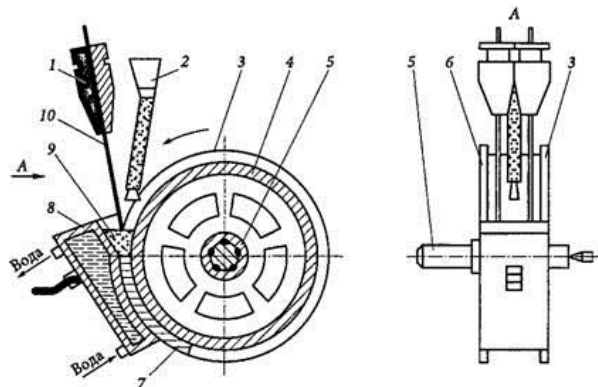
Электрошлаковая наплавка круглой детали: 1 – мундштук; 2 – бункер с флюсом; 3, 6 – боковые держатели флюса; 4 – обод детали; 5 – привод детали; 7 – наплавленный металл; 8 – медный кокиль; 9 – ванна расплавленного флюса; 10 – электрод
